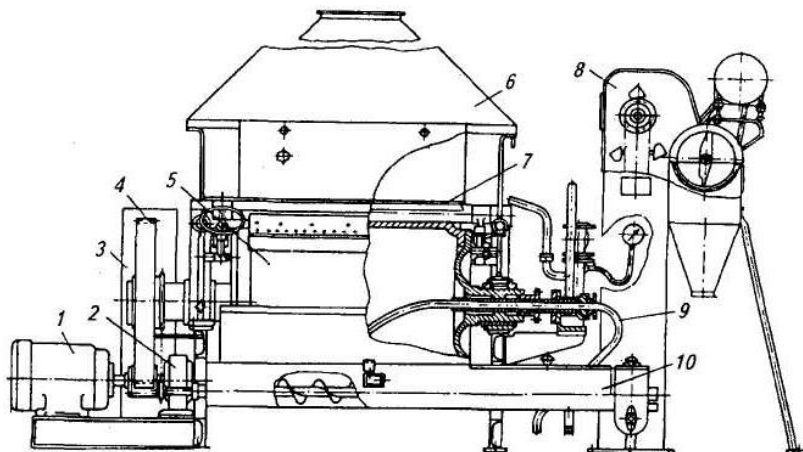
Сушильно-дробильный агрегат СДА-250
